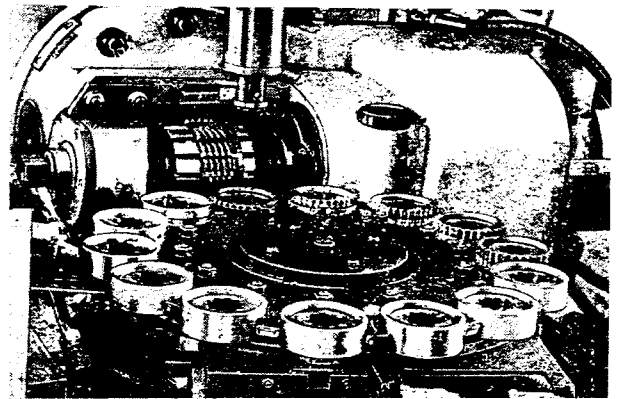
Зубофрезерный станок на базе мод. 5А312 с загрузочным устройством роторного типа
